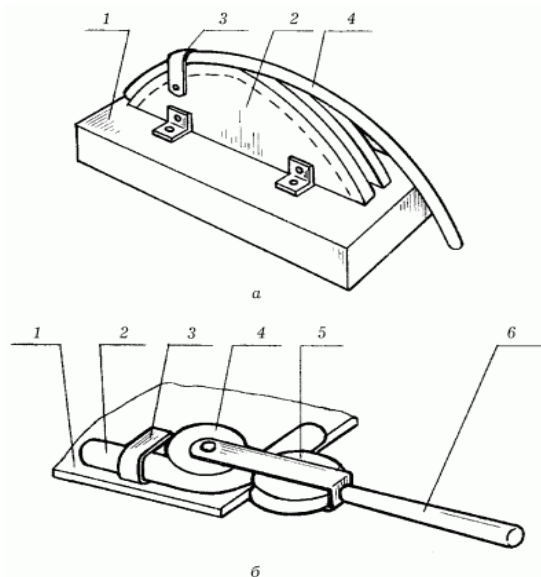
Приспособления для гибки труб: а – плоскопараллельная пластина: 1 – плита; 2 – пластина; 3 – хомут; 4 – труба; б – станок Вольнова: 1 – металлический верстак; 2 – изгибаемая труба; 3 – хомут; 4 – съемный ролик-шаблон; 5 – подвижный ролик; 6 – рукоятка со скобой.
